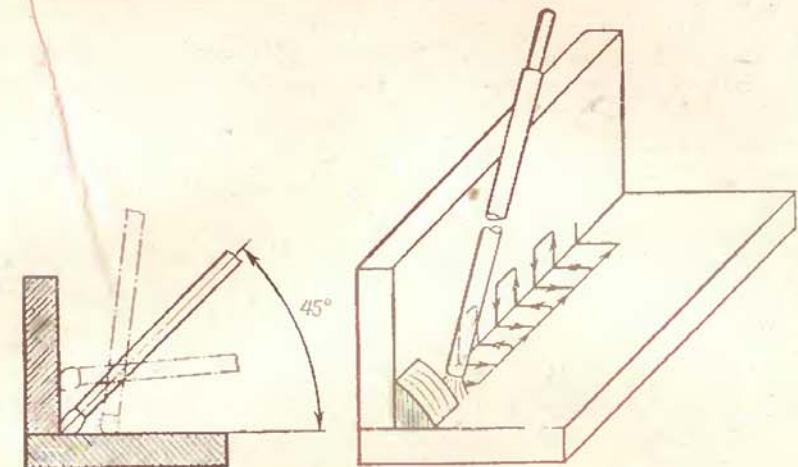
Схема движения конца электрода при сварке углового шва
